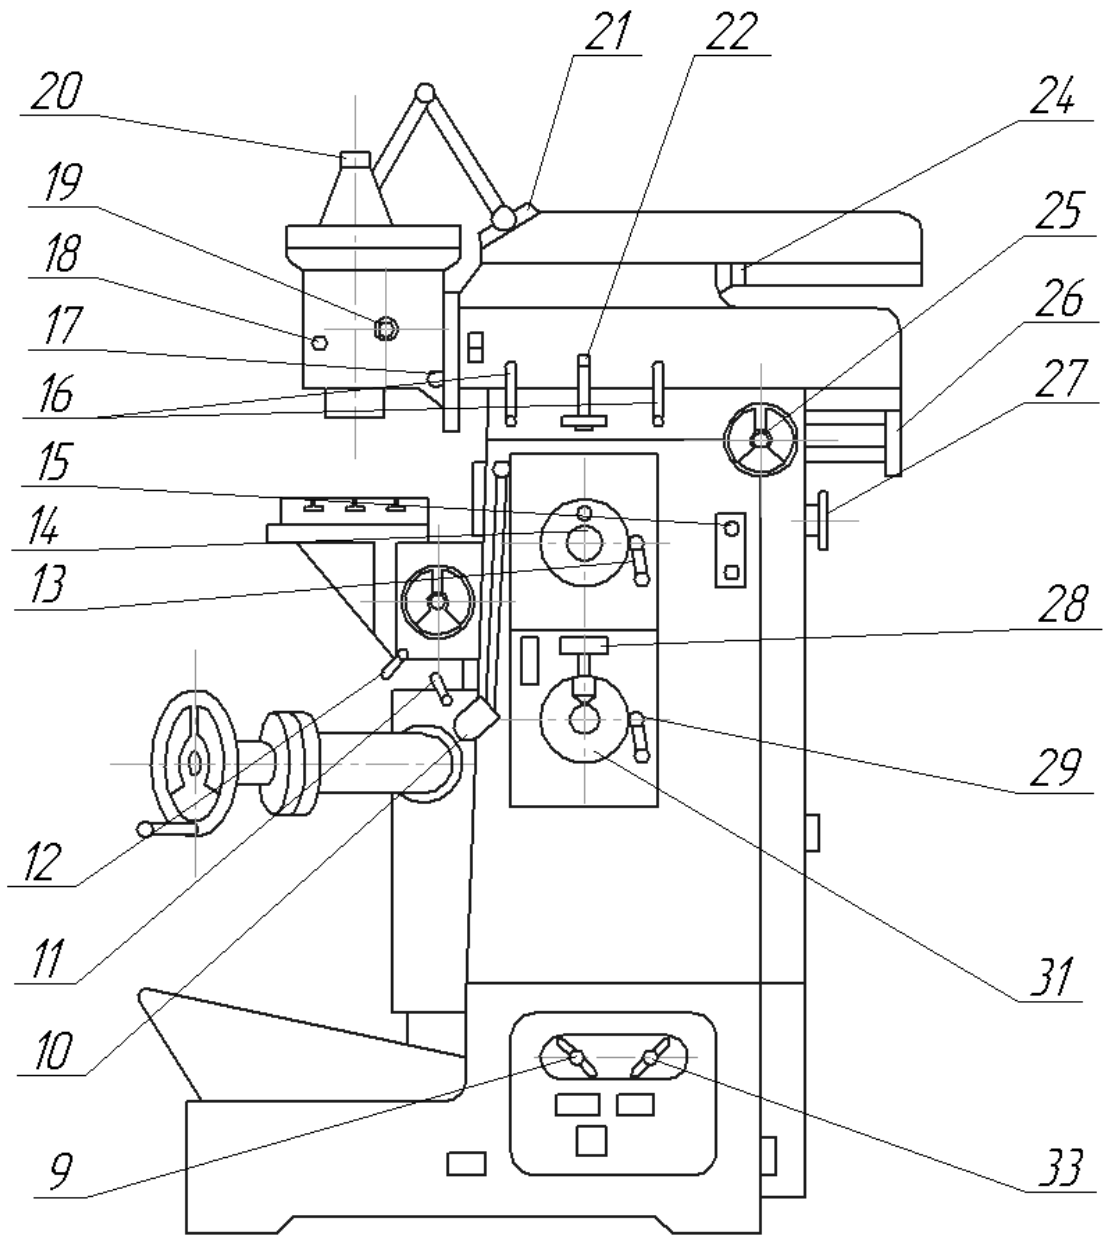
Розміщення органів керування фрезерного верстата
